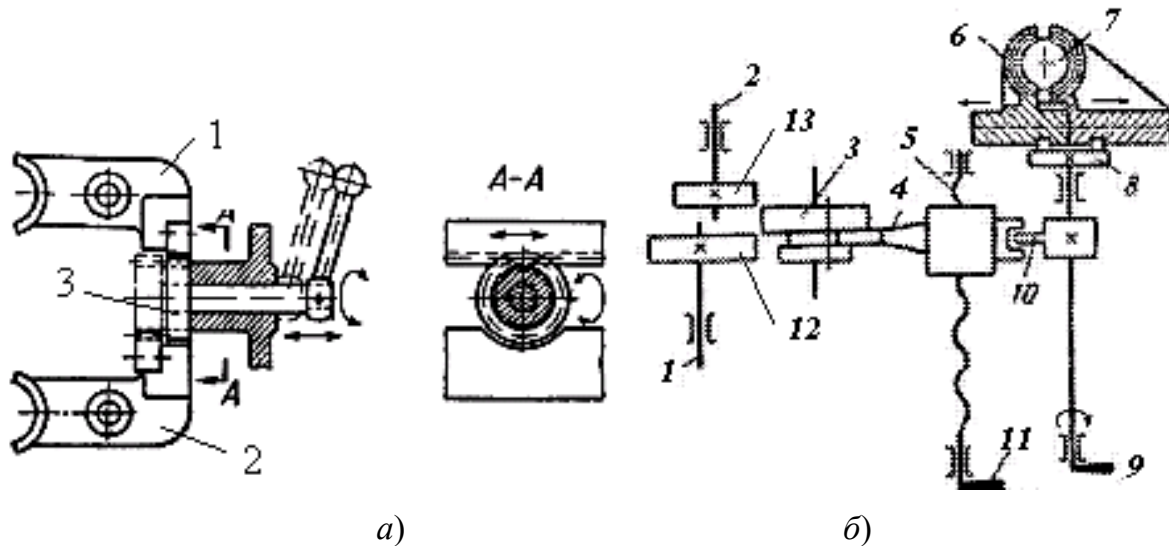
Блокировка деталей управления, движущихся параллельно (а) и одновременного включения ходового вала и ходового винта токарно-винторезного станка (б)
